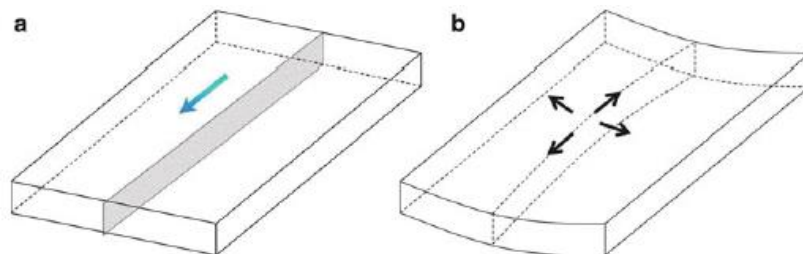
(a) Forma inicial de las piezas a soldar. La región sombreada es la interfaz, mientras que la flecha muestra la dirección de soldadura. (b) Forma final de la pieza debido a la tensión residual. La deformación de la forma durante la soldadura se complica por las fuerzas de sujeción.
